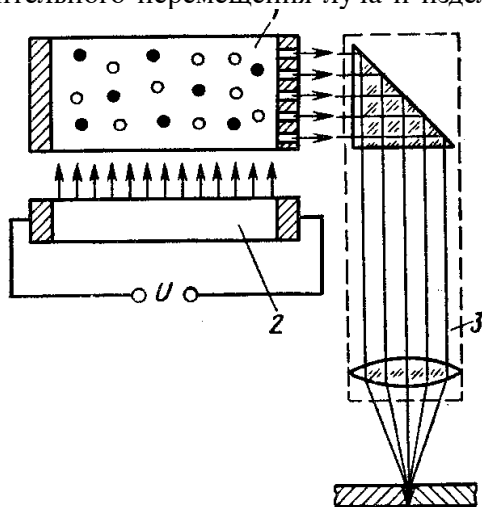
Схема установки для лазерной сварки с твердотельным лазером:
